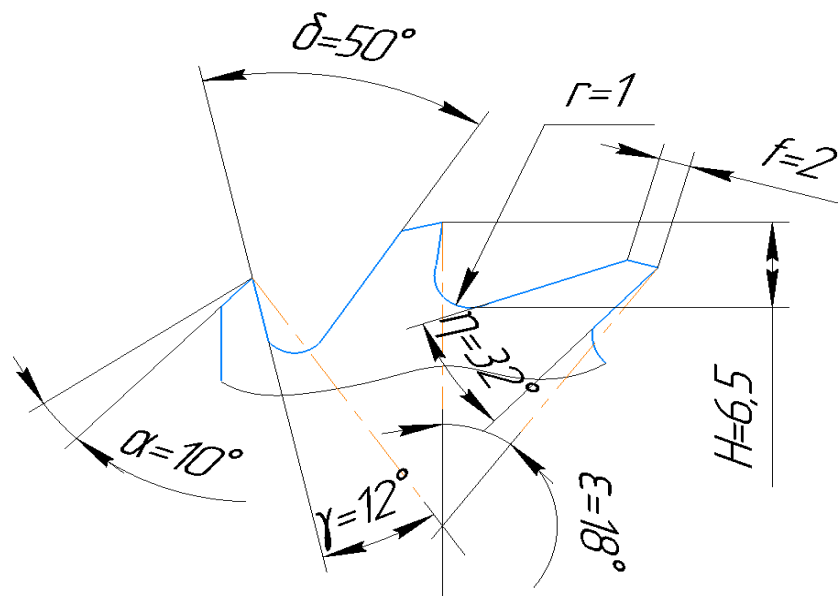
Прийнята геометрія фрези фасонної циліндричної
